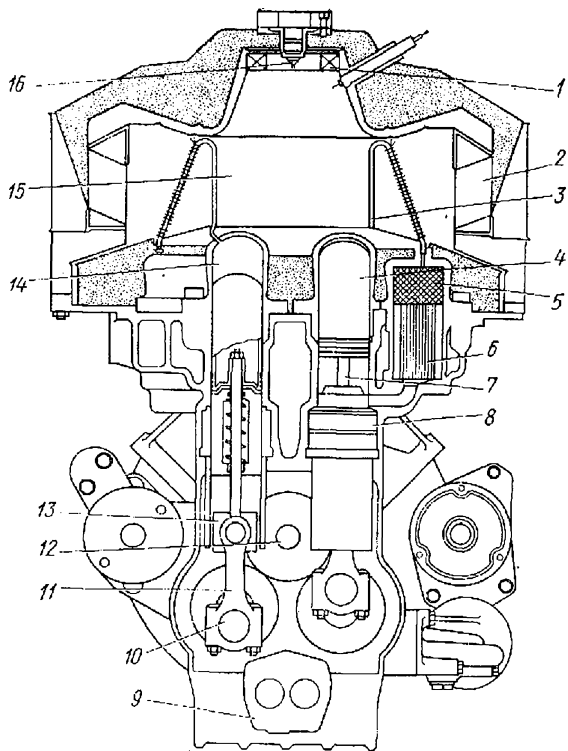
Четырехцилиндровый двигатель Стирлинга двойного действия с параллельно-расположенными цилиндрами фирмы «Юнайтед Стирлинг»:
